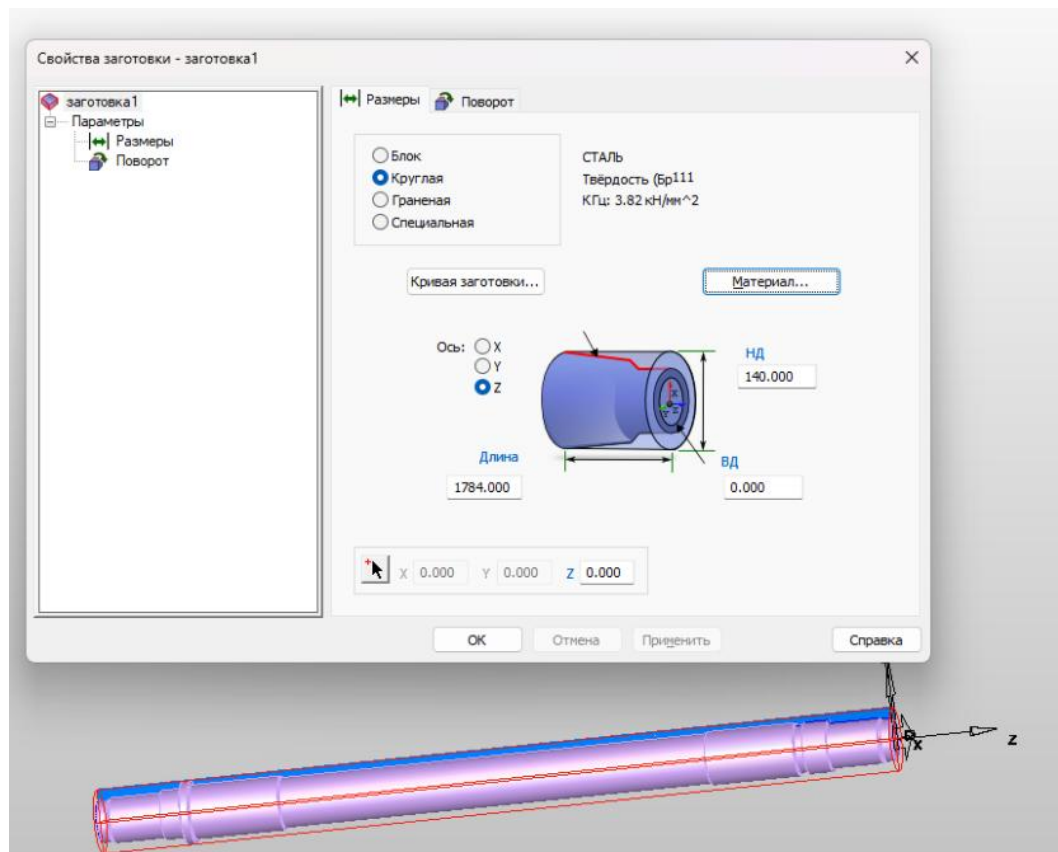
Загальний вигляд імпортування деталі та обраних параметрів заготовки
